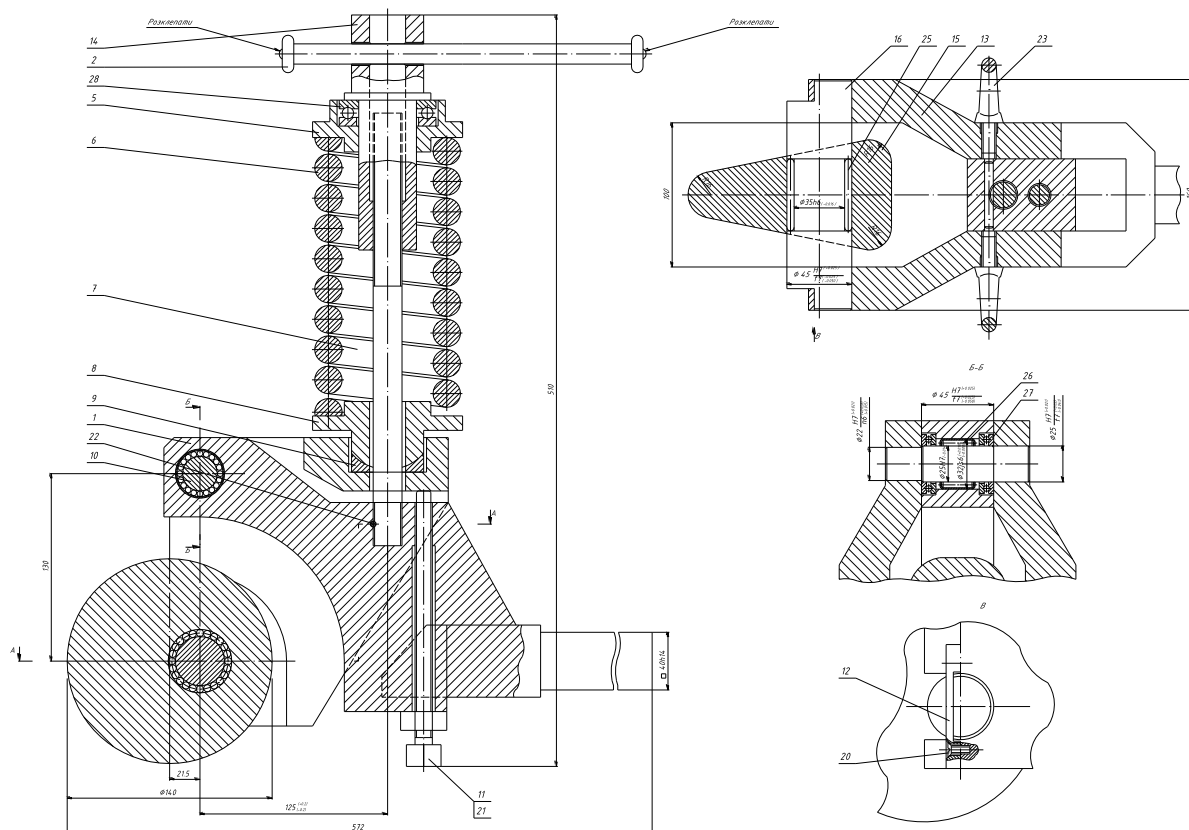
Устройство для обкатывания галтелей клиновидным роликом
